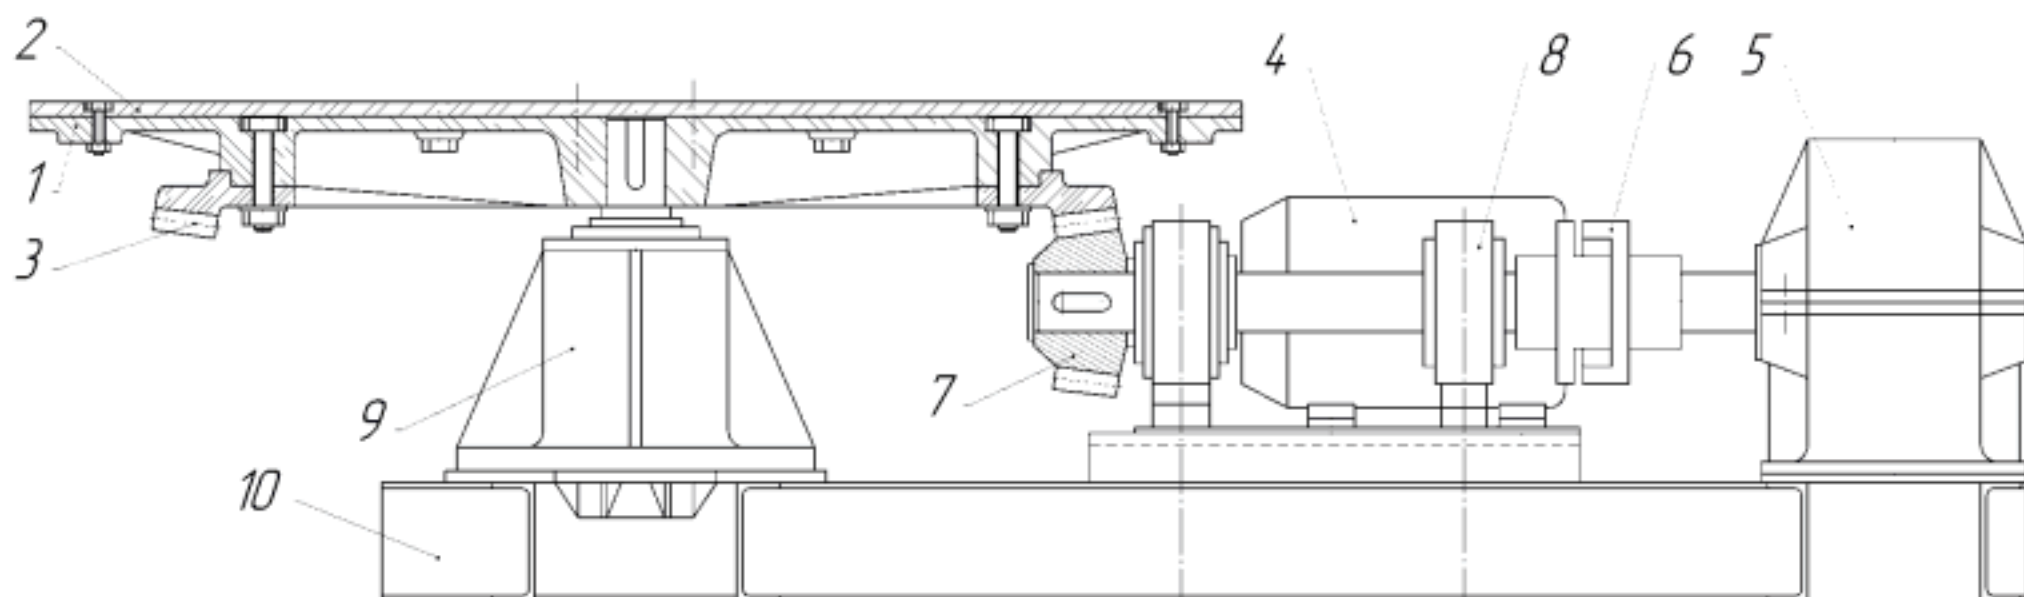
Дісковий живильник з відкритою зубчастою передачею привода: 1 – диск (тарель); 2 – захисна броня; 3 – конічне колесо; 4 – електродвигун; 5 – циліндричний редуктор; 6 – муфта зчеплення; 7 – конічна шестерня; 8 – опорні підшипники; 9 – підп’ятник; 10 – рама
